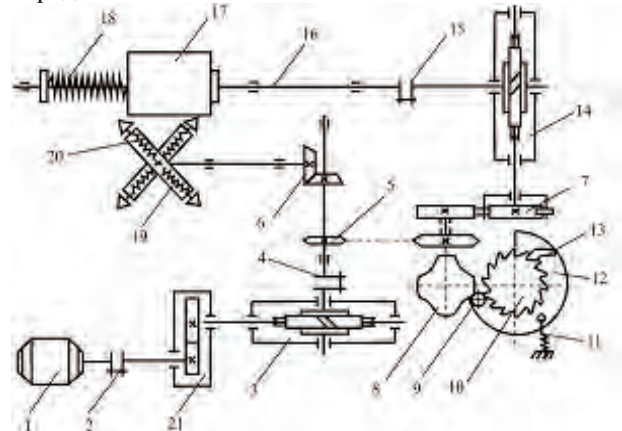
Кинематическая схема привода установки: 1- электродвигатель; 2,4,15 - муфта; 3,14 - редуктор; 5 - цепная передача; 6 - коническая передача; 7 - зубчатая передача; 8, 9, 10,11,12, 13 - элементы механизма дискретного поворота; 16 - вал; 19 - нагружающие пружины; 20 - крестовина.
